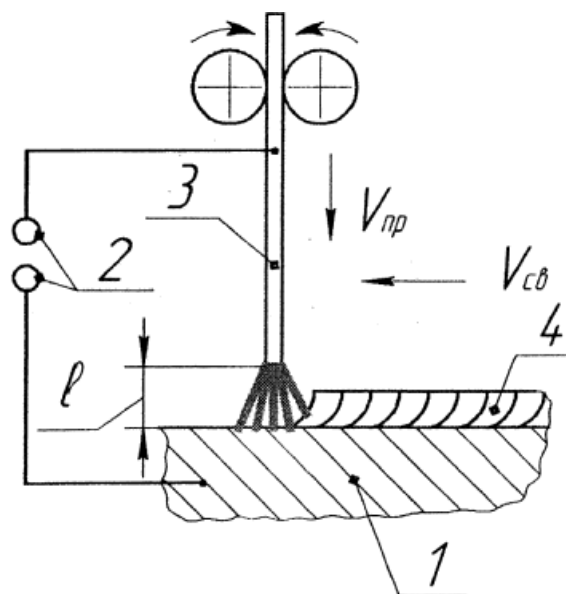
Схема механизированной электродуговой сварки: 1- свариваемое изделие; 2-источник сварочного тока; 3- электродная проволока; 4- сварной шов; $V_{пр}$ - скорость подачи электродной проволоки, м/ч; $V_{св}$ - скорость сварки, м/ч; l - длина сварочной дуги, мм.
